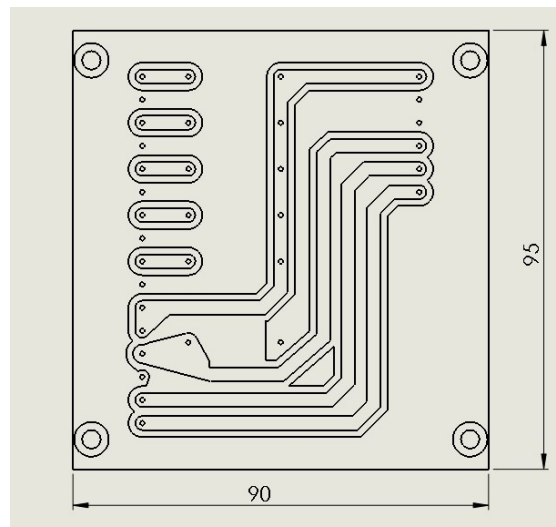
Desenho em CAD das pistas do circuito impresso para maquinação
